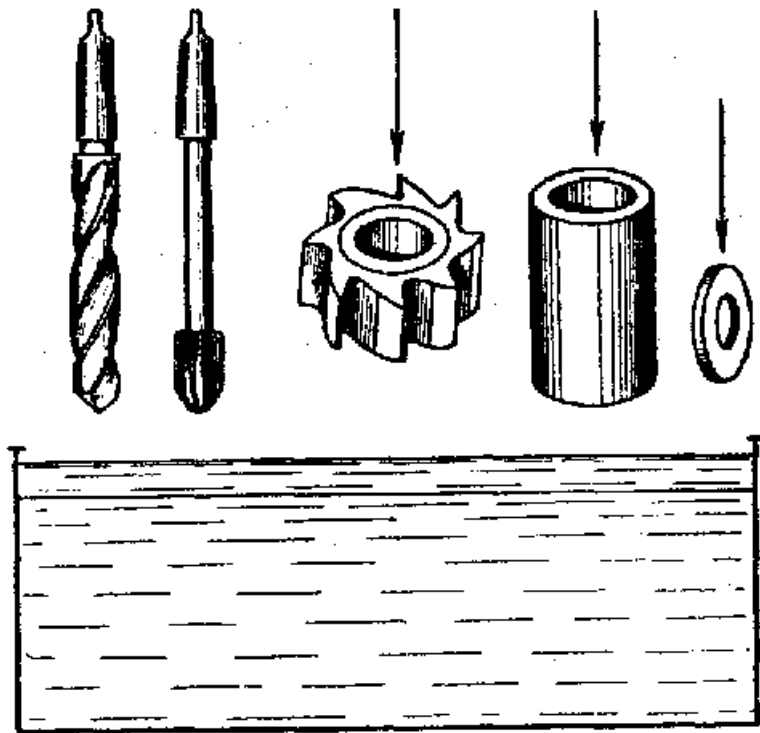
Способи занурення деталей та інструмента у гартівний бак [21]
